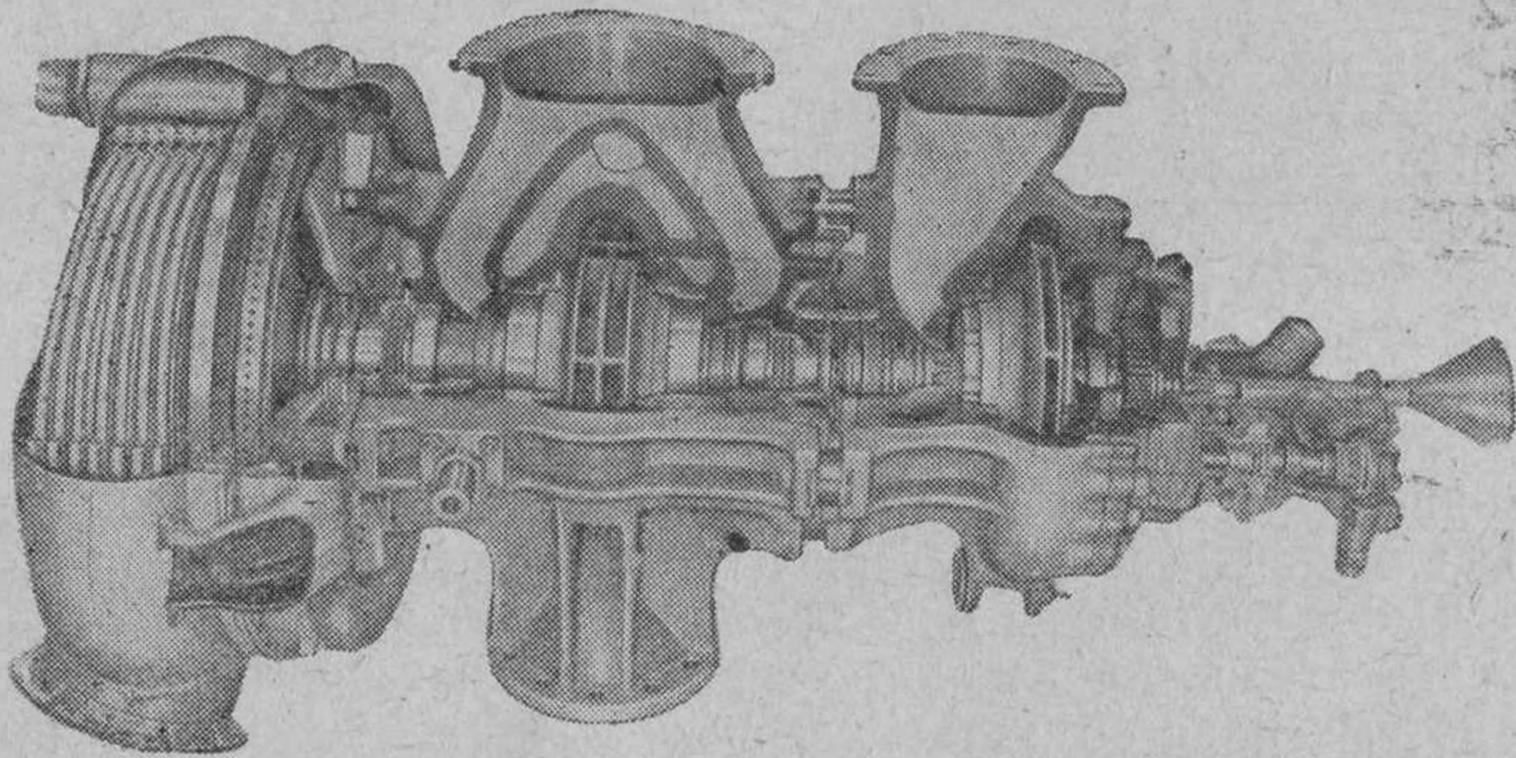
Турбонасосный агрегат двигателя РД-107.
